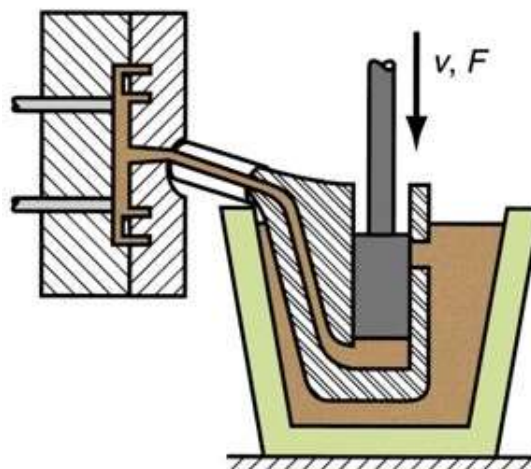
Pistão é empurrado para iniciar a injeção do metal fundido no molde [38]
